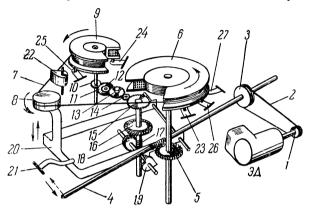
Кинематическая схема механизма магнитофона "Минифон»
